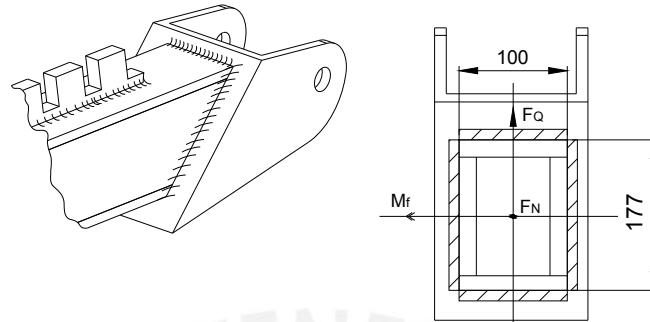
SOLDADURA EN LA BASE DE LA BARRA DE TRACCION
